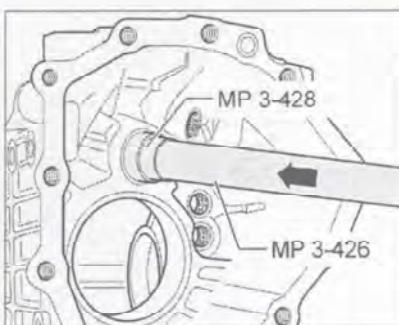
Установка внутренней обоймы игольчатого подшипника.
